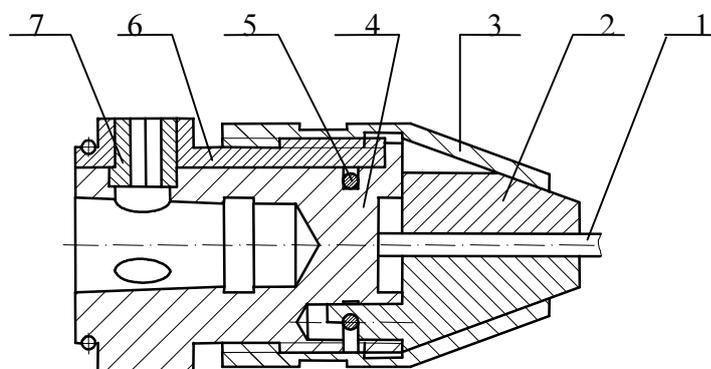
Эксцентриковый сверлильный патрон с ключом
